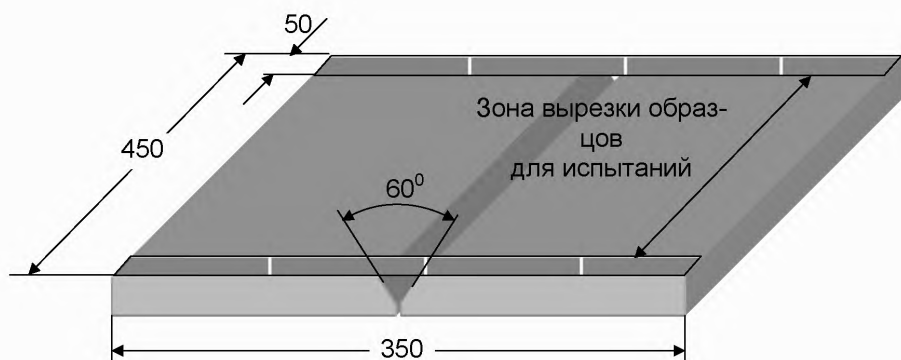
Контрольные сварные соединения типов V; X.
